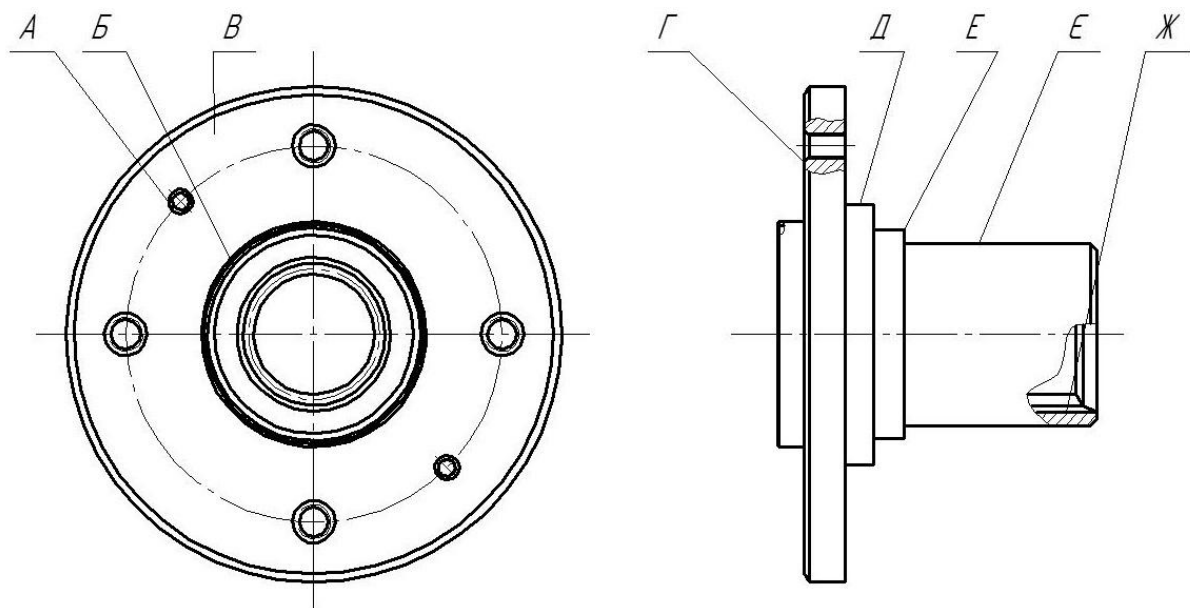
Конструкція маточини переднього колеса автомобіля із позначенням контрольованих поверхонь.
